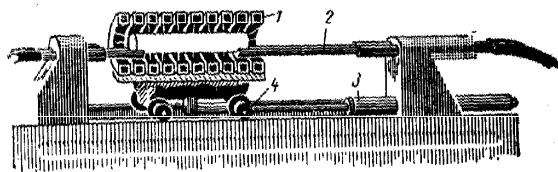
Схема периодического нагревателя с подвижным индуктором:
